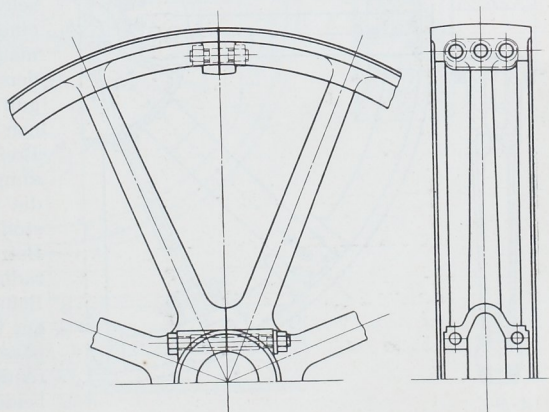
Zwischen den Armen geteiltes, an der Fuge bearbeitetes Rad.
